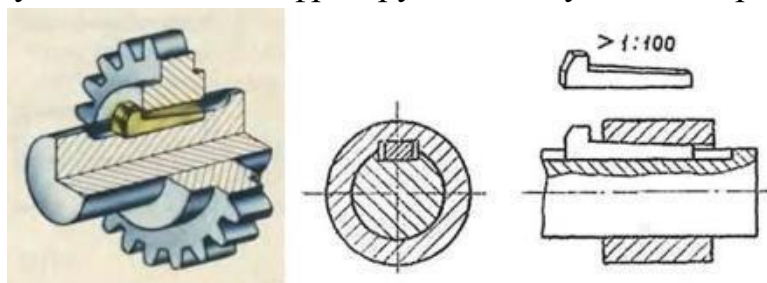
Соединение клиновой шпонкой: вид и чертеж
